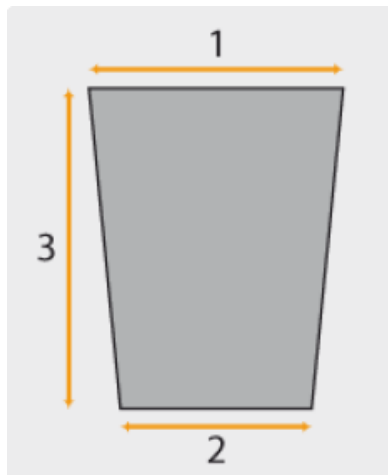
Розміри листової заготовки поліпропілену:
